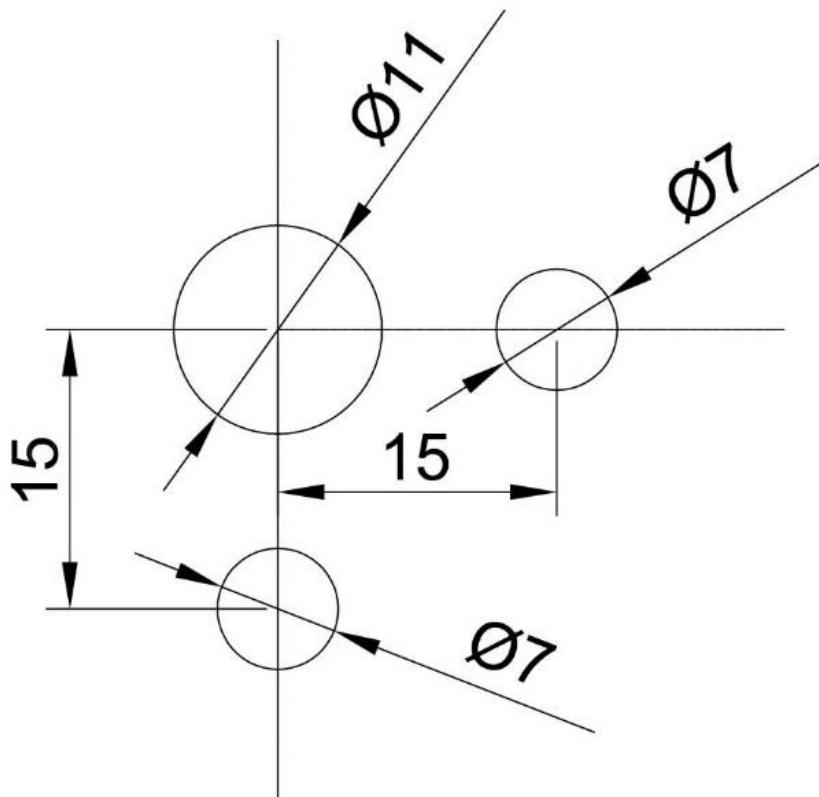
«Разметка отверстий крепления кронштейнов 400 кг и 630 кг»
